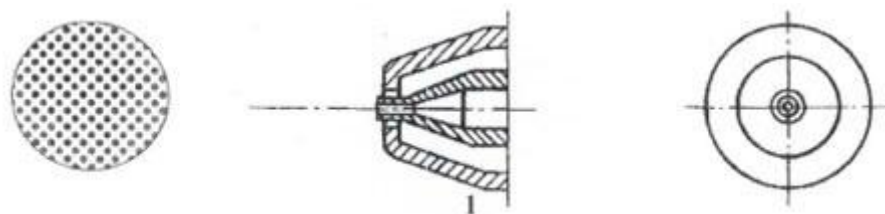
Круглый след (слева), конструкция распылительной головки (по центру) и вид головки спереди (справа).
